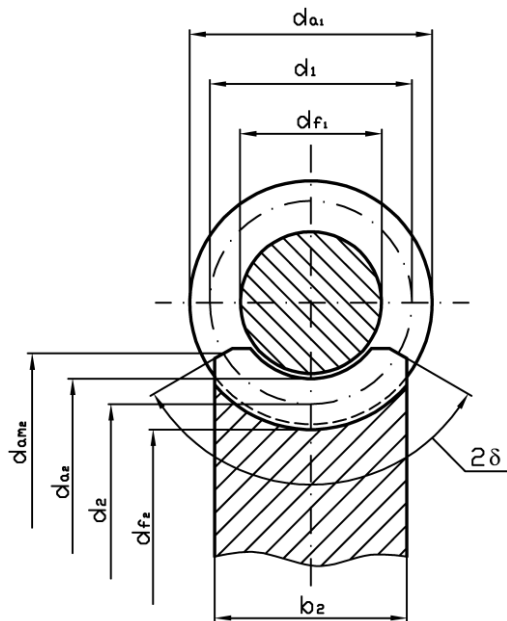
Схема зацепления червячной цилиндрической передачи
